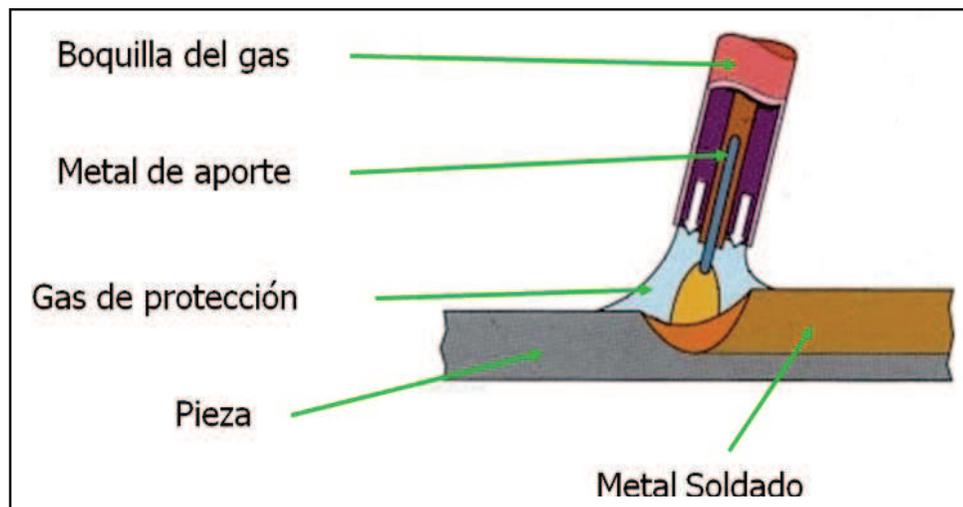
Proceso de Soldadura GMAW.
